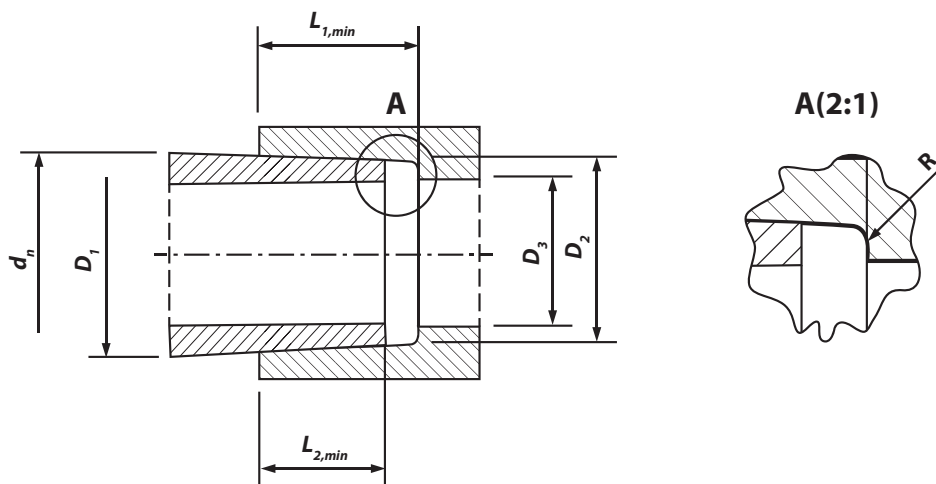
Габаритные размеры раструба сварных фитингов
